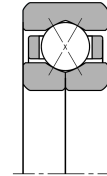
Vierpunktlager mit geteiltem Innenring [12]
